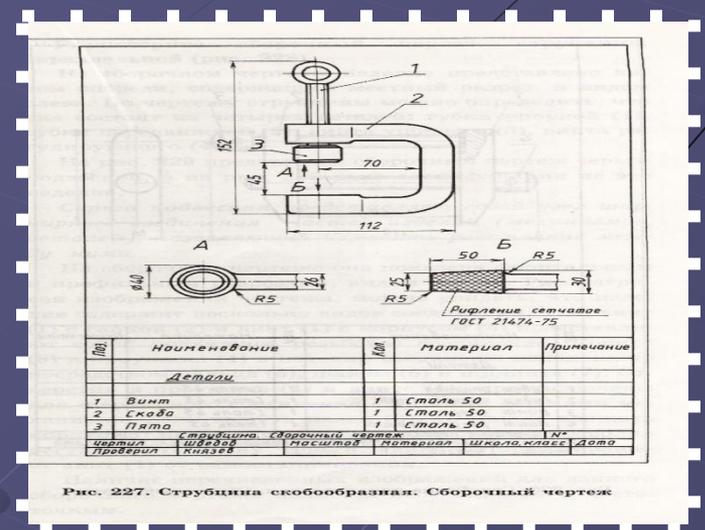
Струбцина скобообразная. Сборочный чертеж
